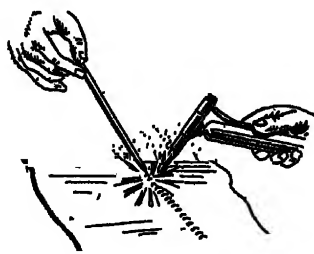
Tenue du métal d'apport et du chalumeau pour la soudure des tôles d'aluminium minces.
